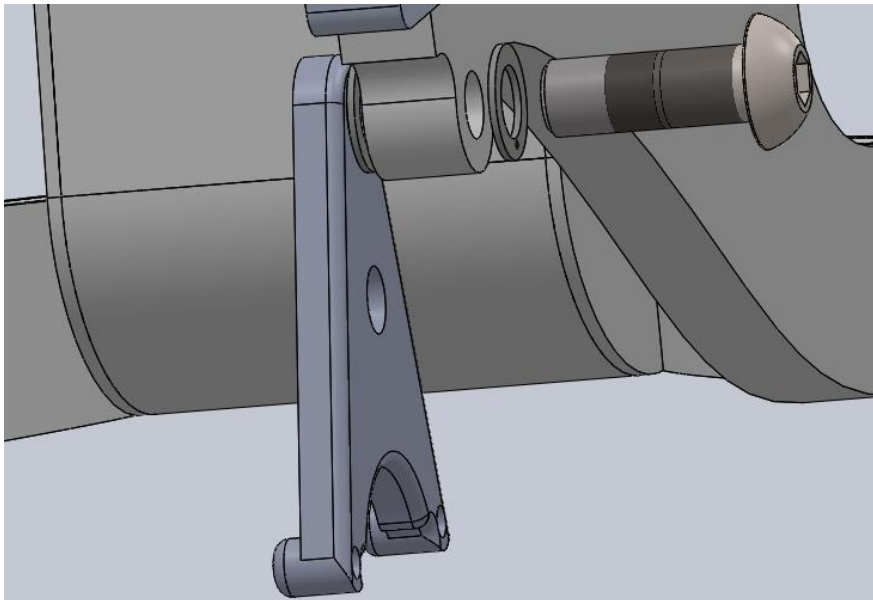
Explosionado de la sujeción del soporte de la pinza de freno . [2]
